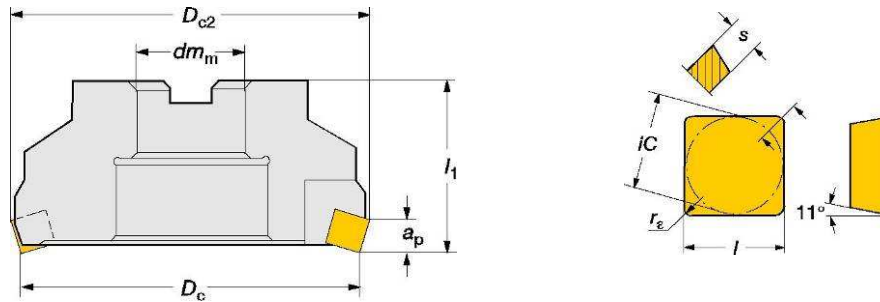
Détails de l'outil fraise et de la plaquette.
